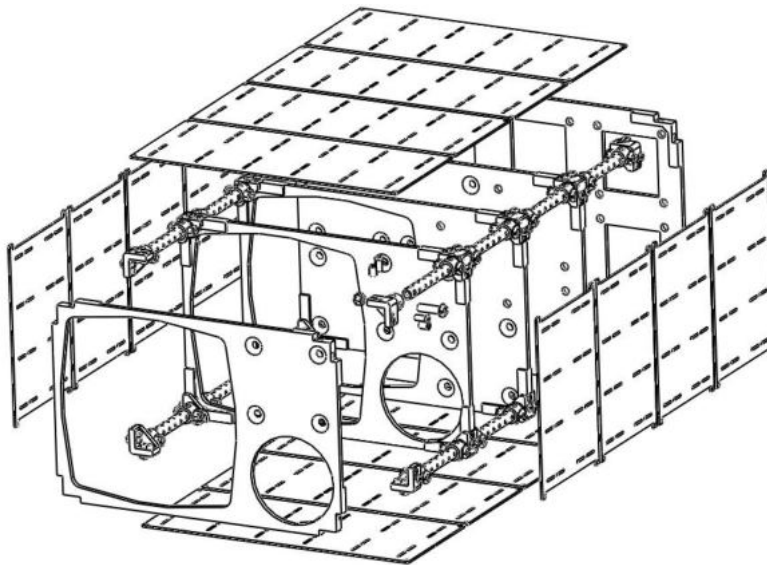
Вид конструкции корпуса с разнесёнными частями
